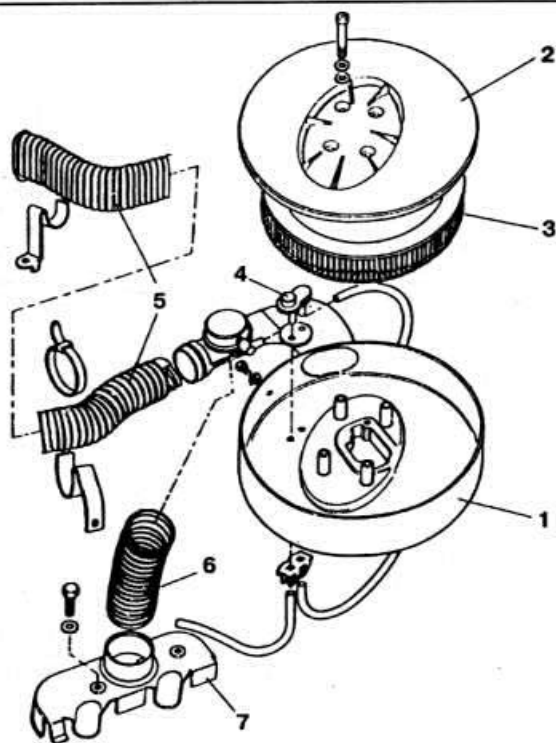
Воздушный фильтр карбюраторных двигателей «REC» и «NEL»:
